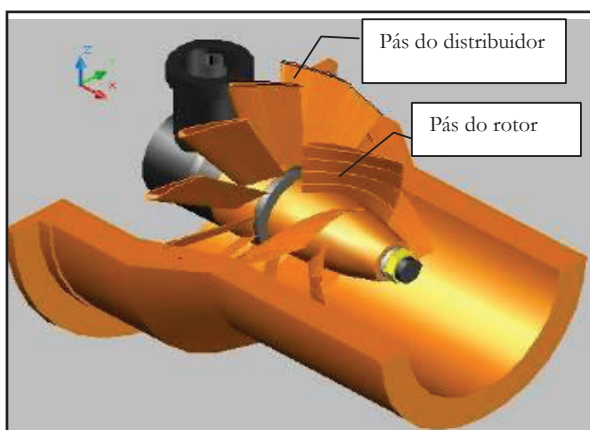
Corte esquemático de turbina hidráulica axial mostrando distribuidor e rotor
